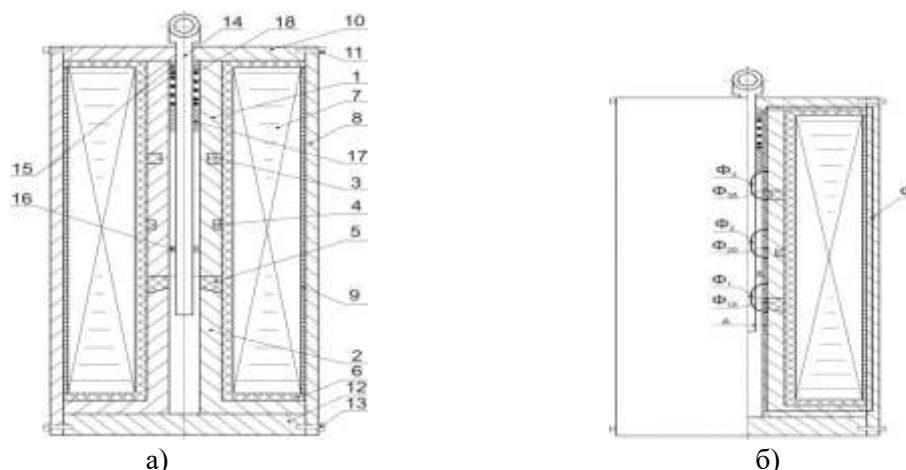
Линейный электродвигатель: а – конструкция, б – принцип действия
